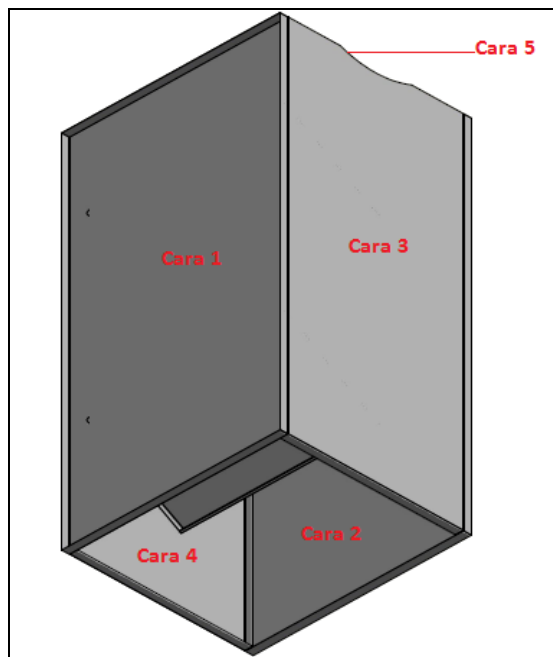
MONTAJE DE LAS CHAPAS METÁLICAS Y PLANOS INCLINADOS.
